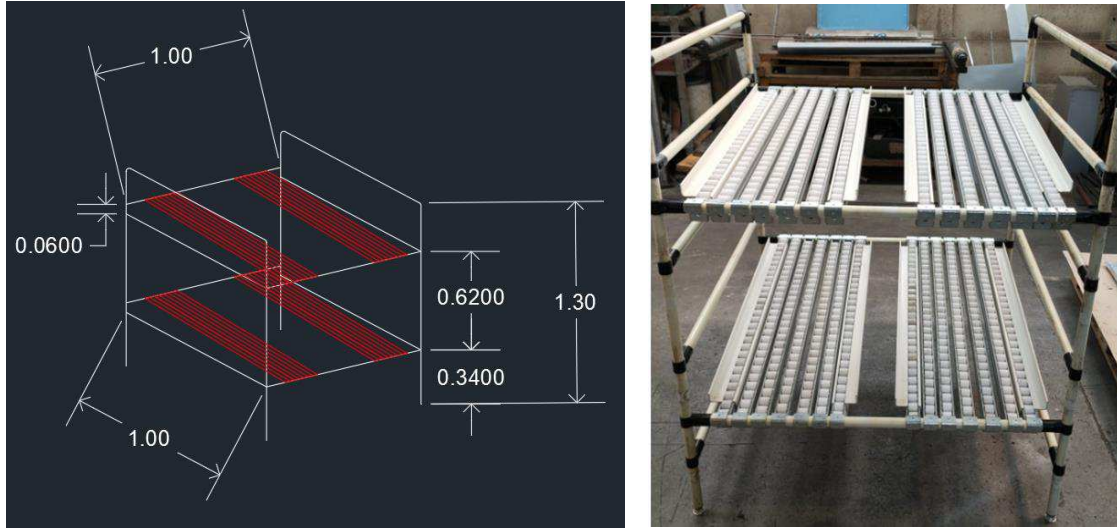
Disegno e realizzazione buffer per piedi e ruote frigo
